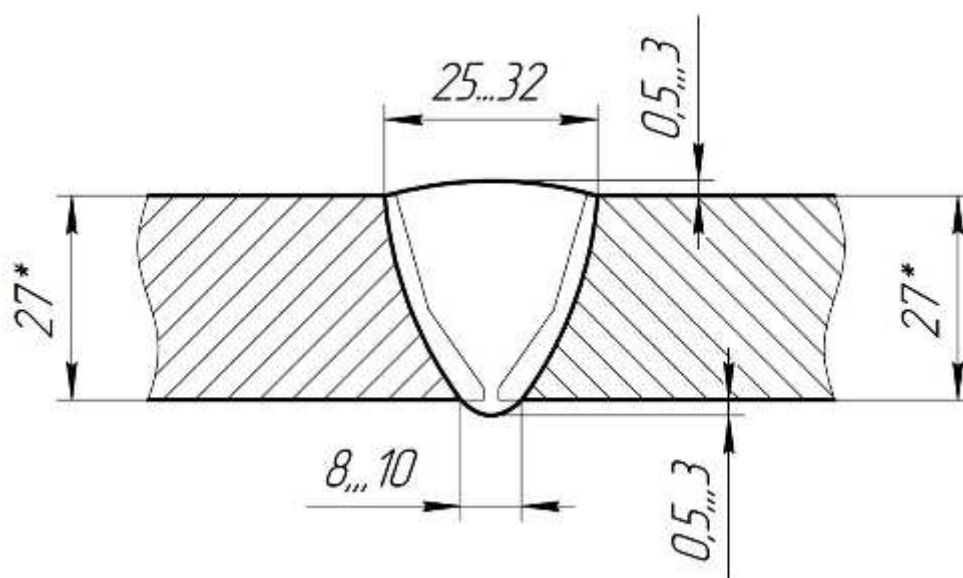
Общий вид сварного шва, сваренного автоматической сваркой в среде защитных газов
